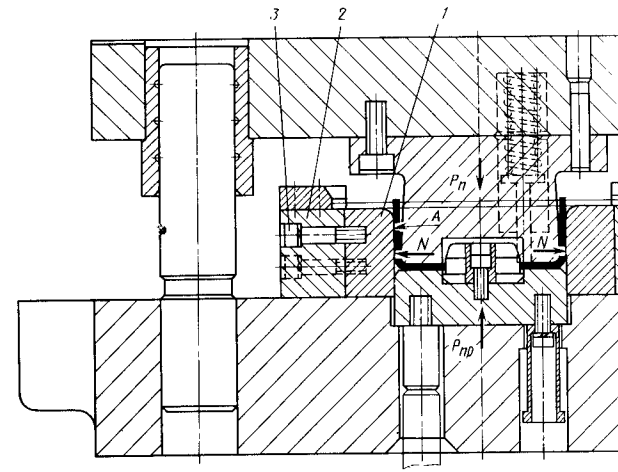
Разрез типовой конструкции штампа для U-образной гибки листовой заготовки
